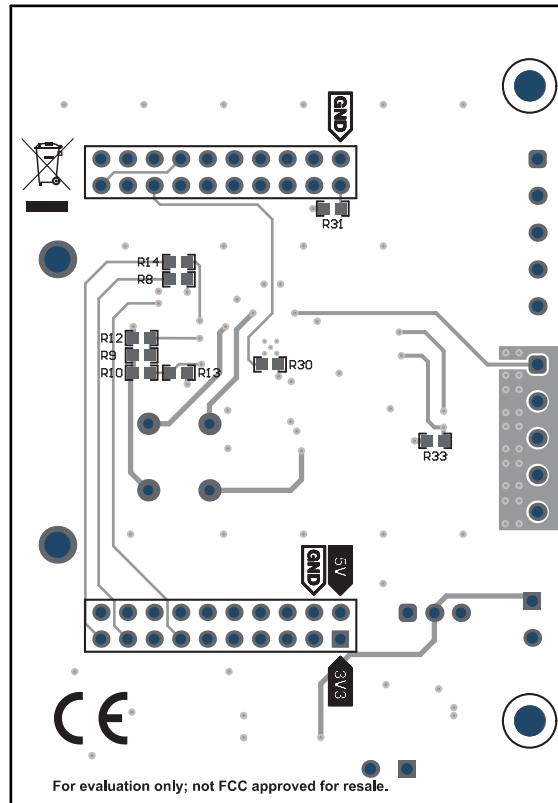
ADS122x14EVM の PCB レイアウト(下面図)
